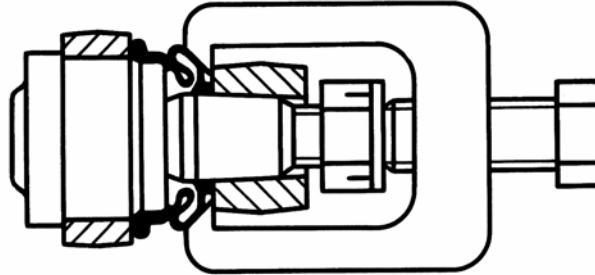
Выпрессовка пальца шарнира рулевых тяг универсальным съемником
